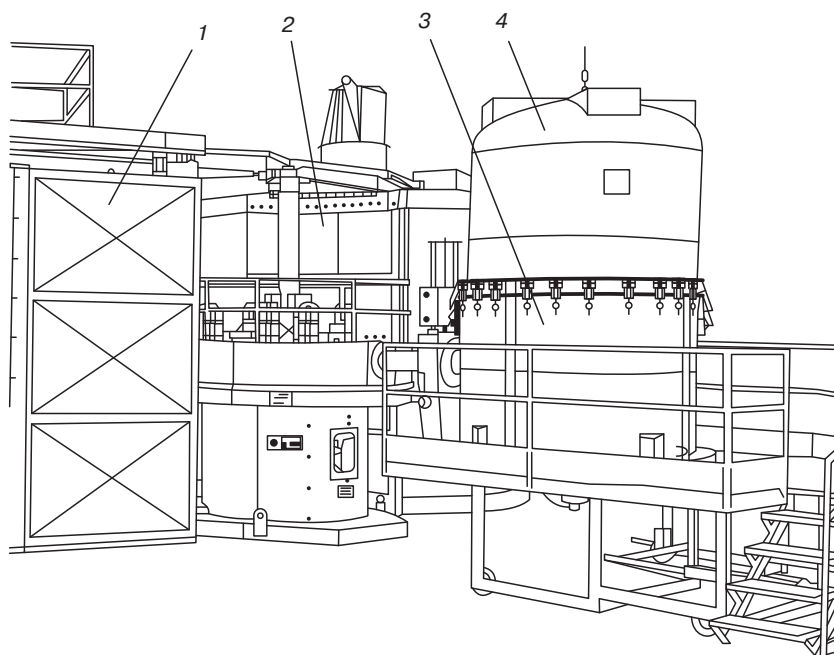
Общий вид установки для производства крупногабаритных изделий методом ротационного формования: 1 — термокамера; 2 — привод, обеспечивающий вращение форм; 3 — форма; 4 — изделие
